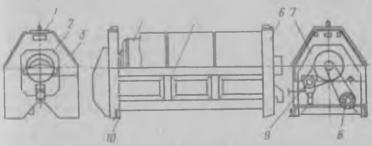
Цилиндрический сегментный триер ТК-4: 1. 3, 7—ограждения; 2—течка: 4— цилиндр; 5—рама; 6— приемини; 8 привод; 9— механизм регулирования частоты вращения цилиндра; 10 опора
